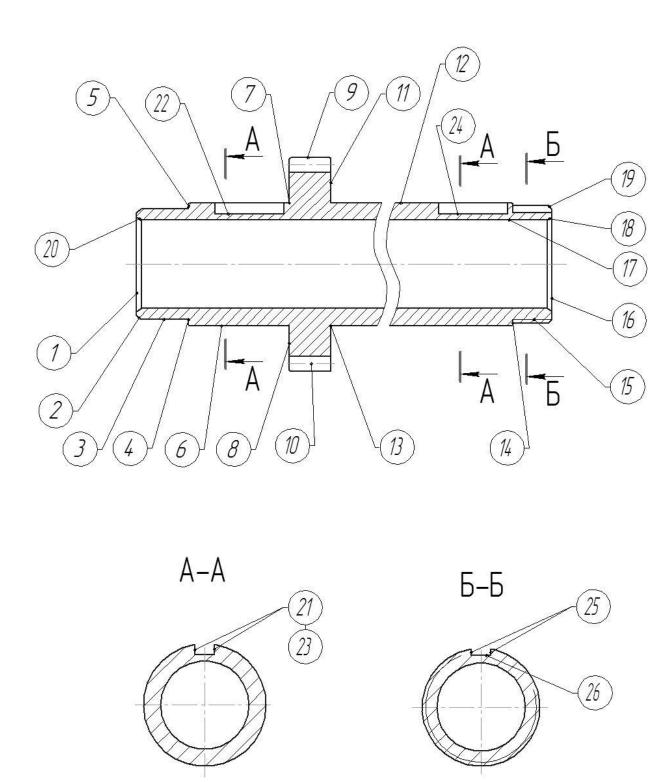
Классификация поверхностей детали вал-шестерни редуктора двухшнекового экструдера
